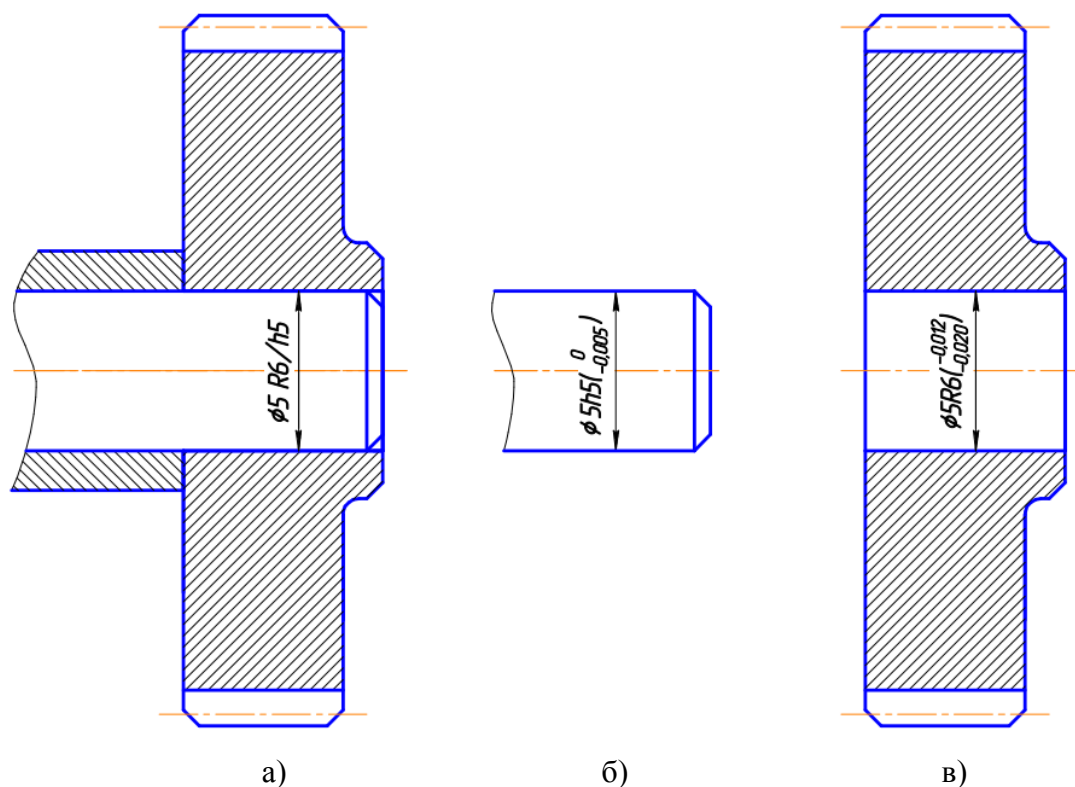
Эскизы деталей: а) соединение; б) вал; в) колесо зубчатое
